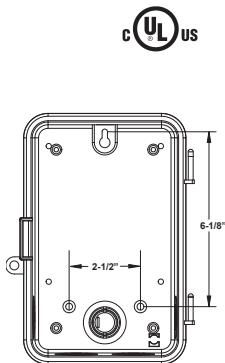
Vue arrière du boîtier et dimensions des orifices de montage
